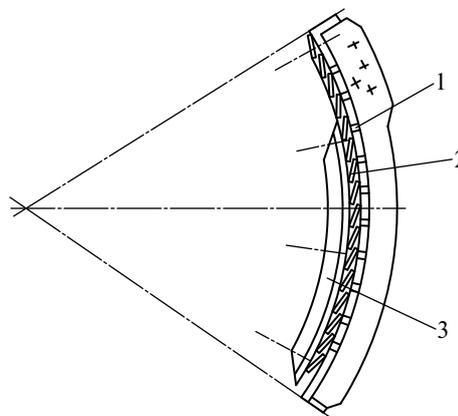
Схема решетки с терочной поверхностью: 1 — решетка; 2 — терочная поверхность; 3 — винтовой направлятель
